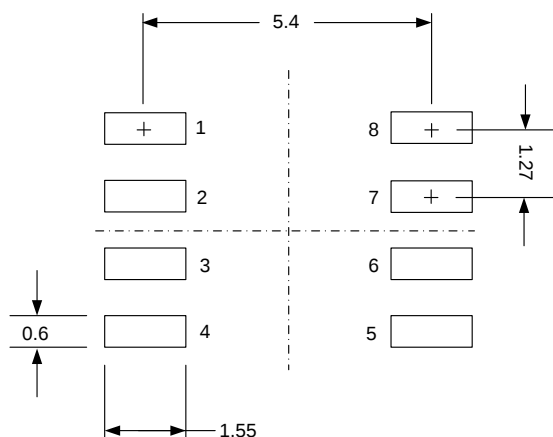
PCB 焊盘: 8-引脚 SOP
